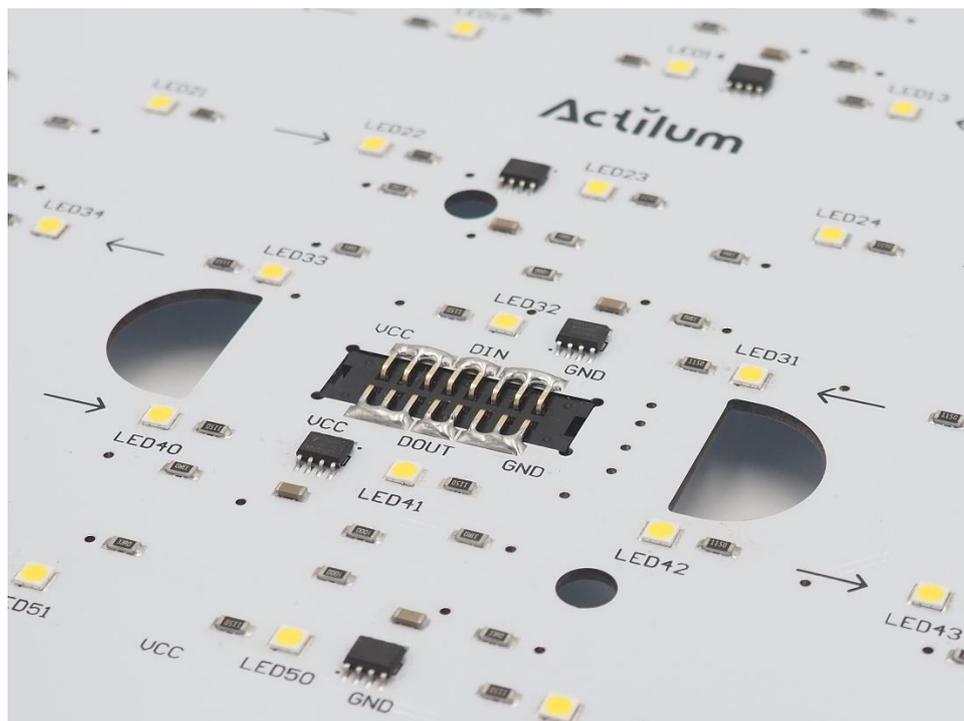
PCB píxel Blanco detalle conector y agarres vista delantera.
